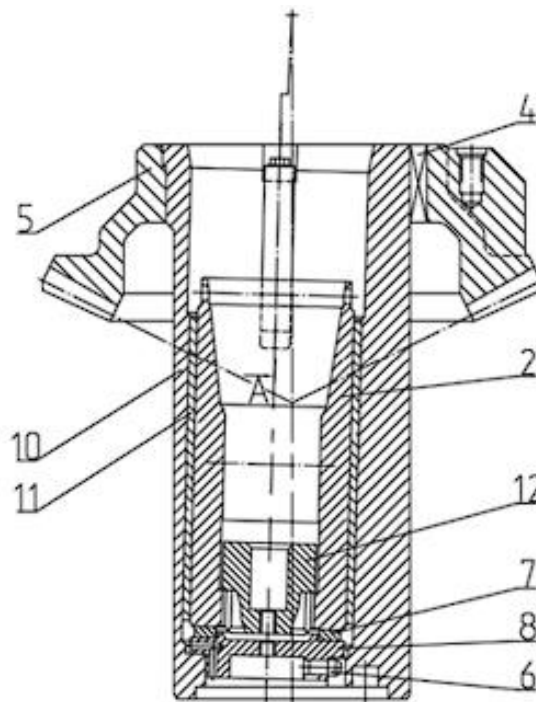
Складові елементи ексцентрикового вузла дробарки: 1 – шпонка; 2 – стакан; 4 – клинова шпонка; 5 – зубчасте колесо приводу; 6 – фіксуючий дюбель; 7 – опорний диск; 8 – підп'ятник; 9 – стопорна шайба; 10 – корпус ексцентрика; 11 – втулка; 12 – вкладиш; 13 – болт кріплення
